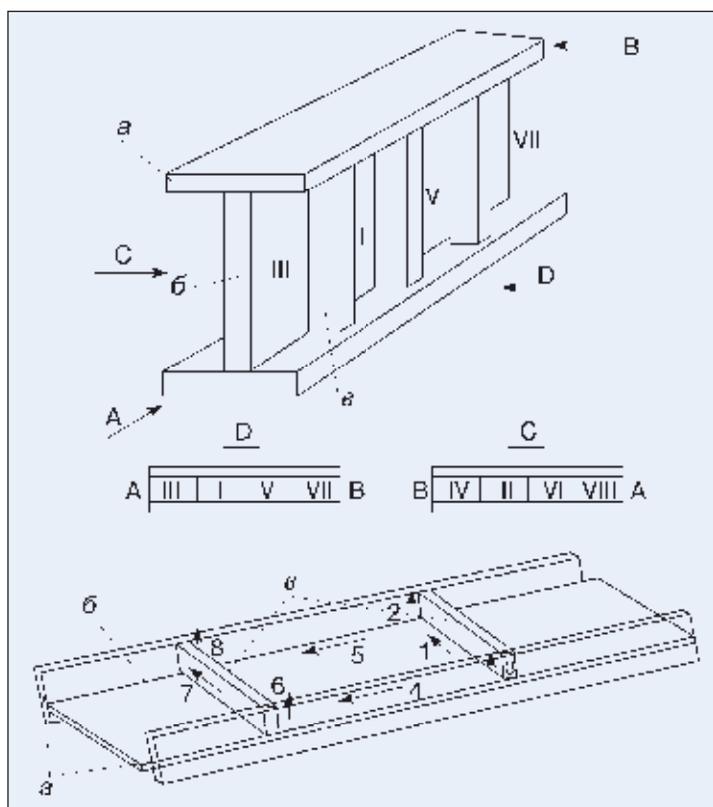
Сварка двутавровой балки с ребрами: а — полка; б — стенка; в — ребро
